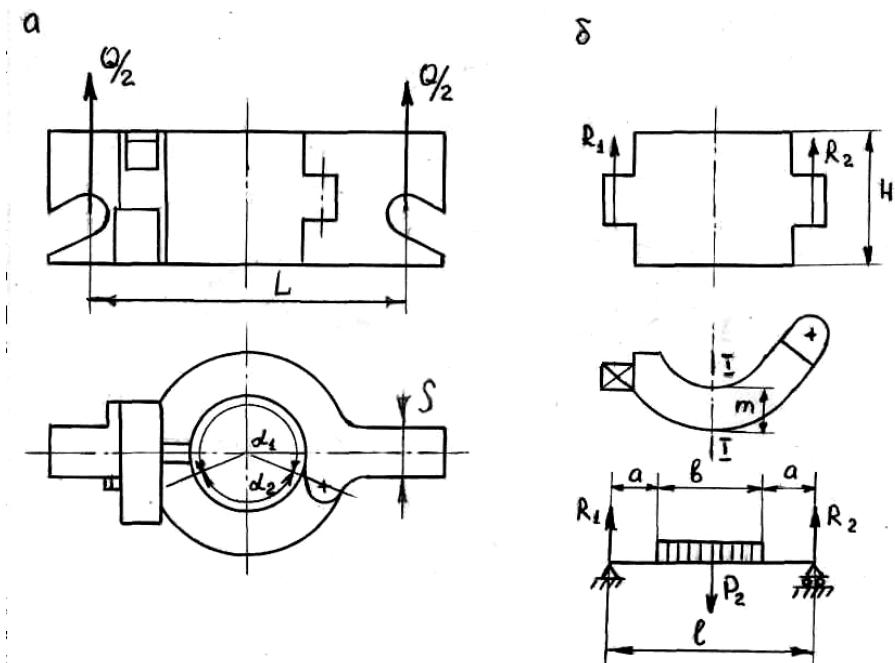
Расчётная схема элеватора: а) корпус; б) затвор
